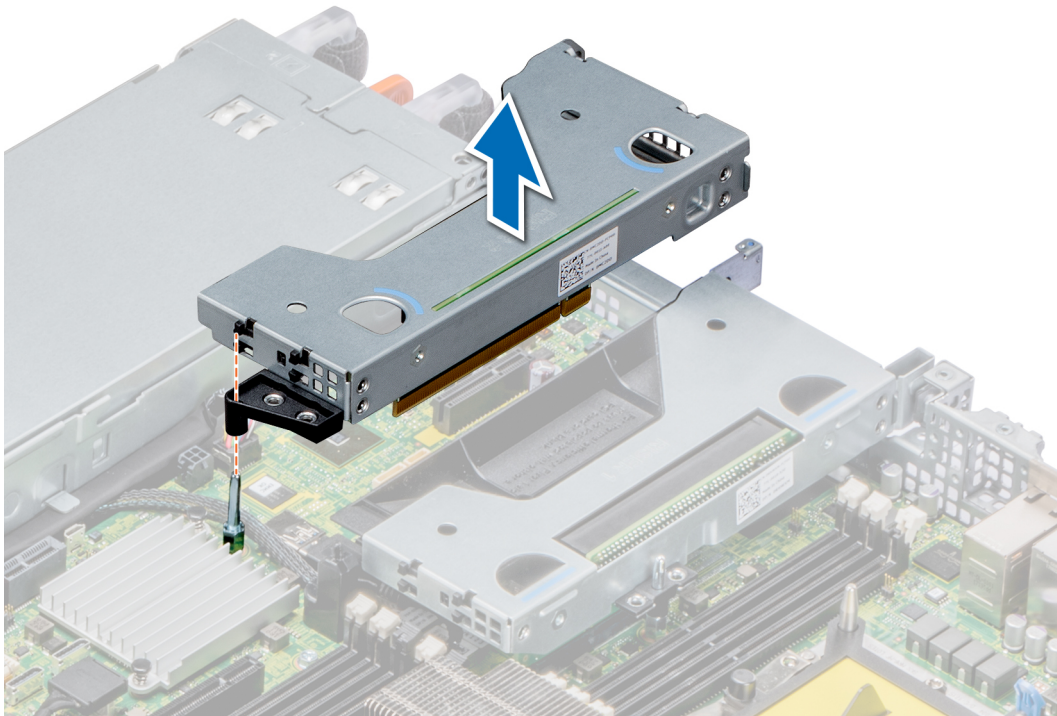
Extracción del soporte vertical izquierdo de perfil bajo (soporte vertical 2)
